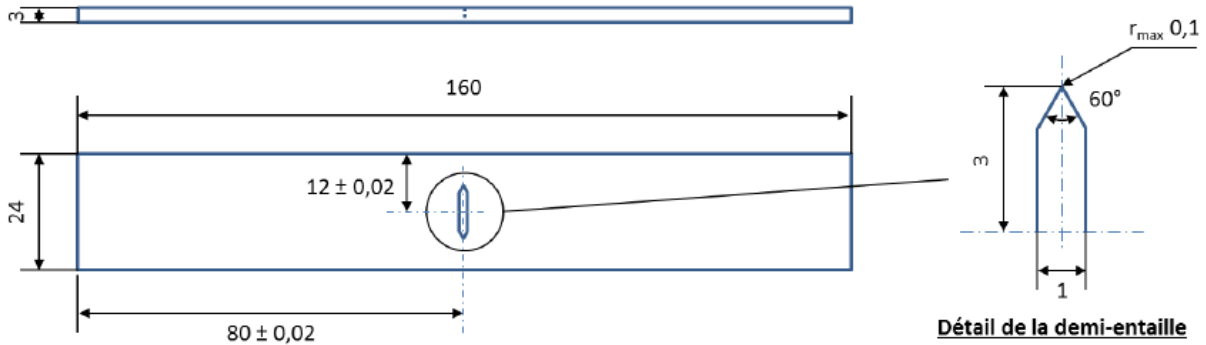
Géométrie et dimensions millimétriques des éprouvettes TFC en aluminium 7075-T6
